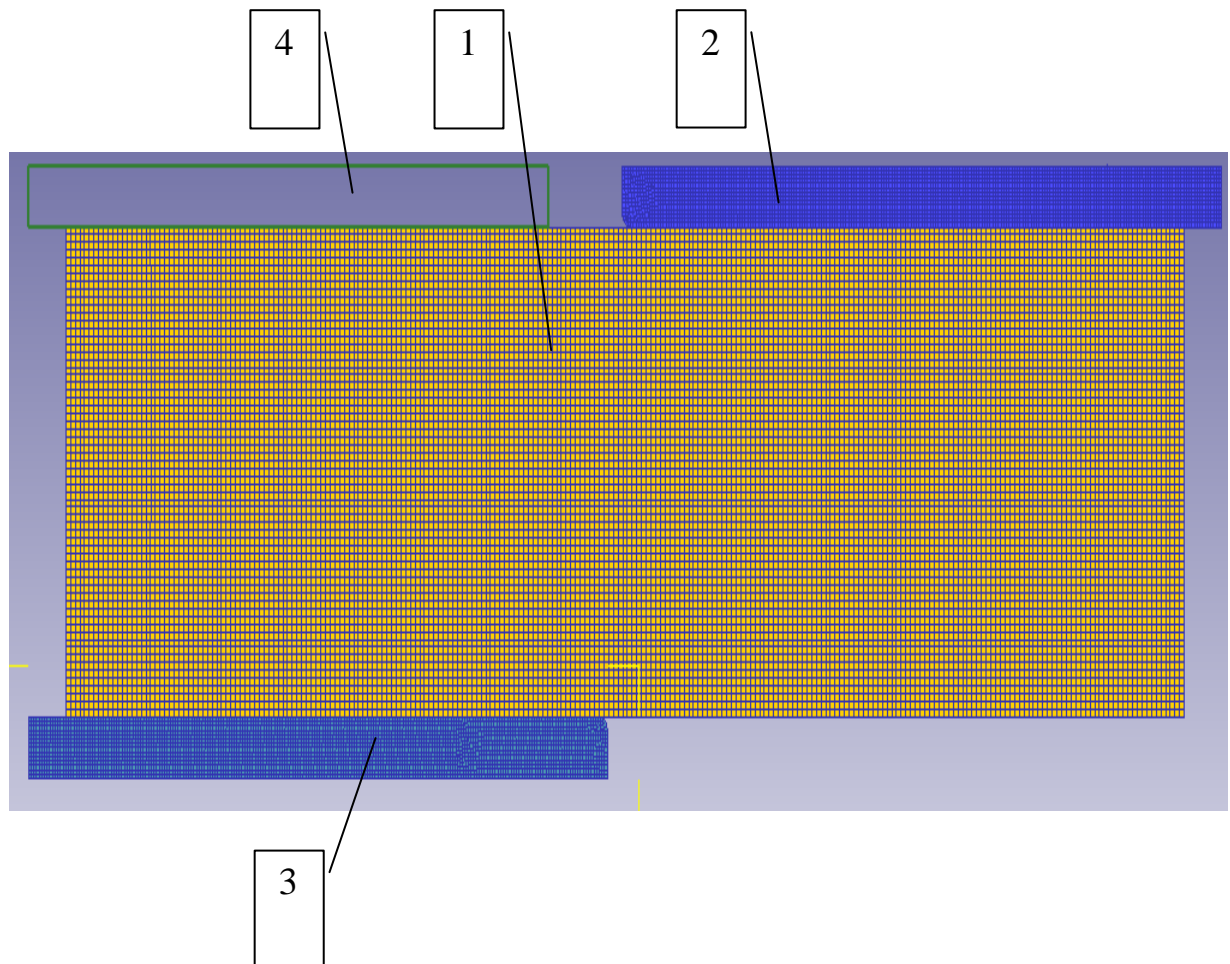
Схема расположения частей штампа: 1 – заготовка;
